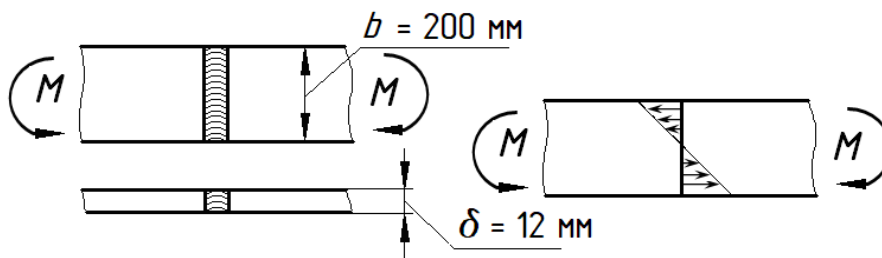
Размеры и расчетная схема стыкового сварного соединения
